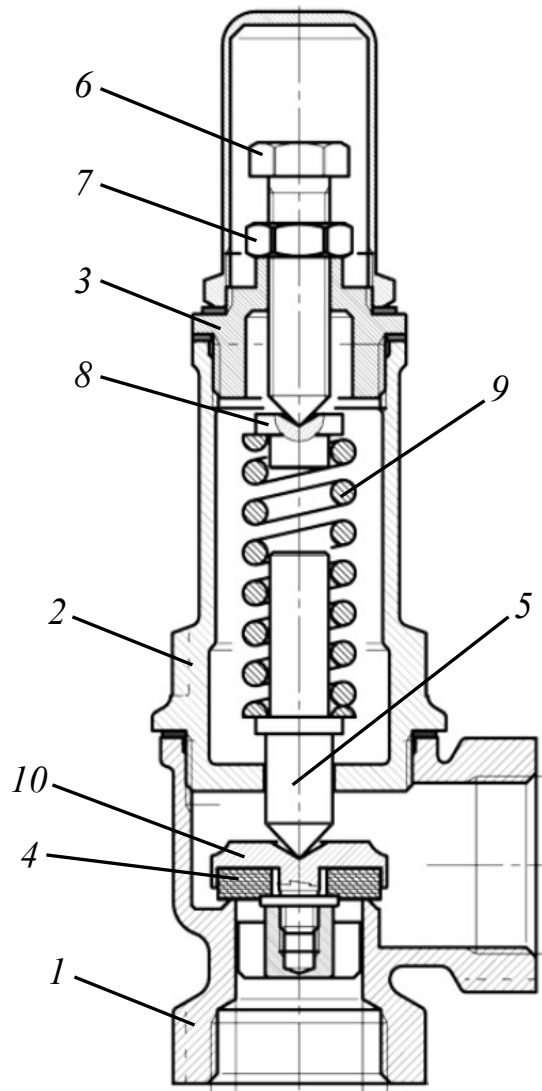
Схема запобіжного клапана прямої дії: 1 – корпус; 2 – кожух; 3 – кришка; 4 – диск; 5 – стрижень; 6 – гвинт регулювання; 7 – гайка; 8 – шайба; 9 – пружина; 10 – сідло
